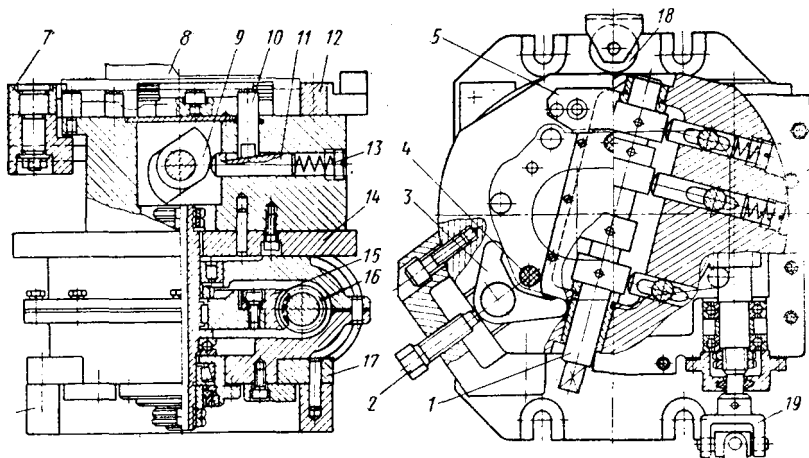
Фрезерное приспособление с механизацией поворота заготовки
